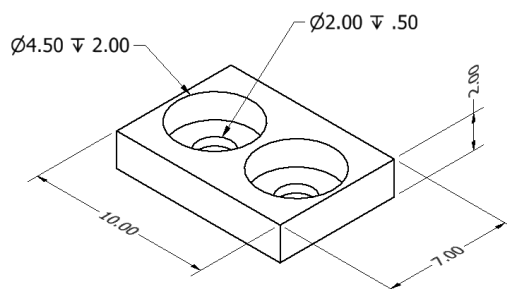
Dimensões da seção de posicionamento e fixação da fibra
